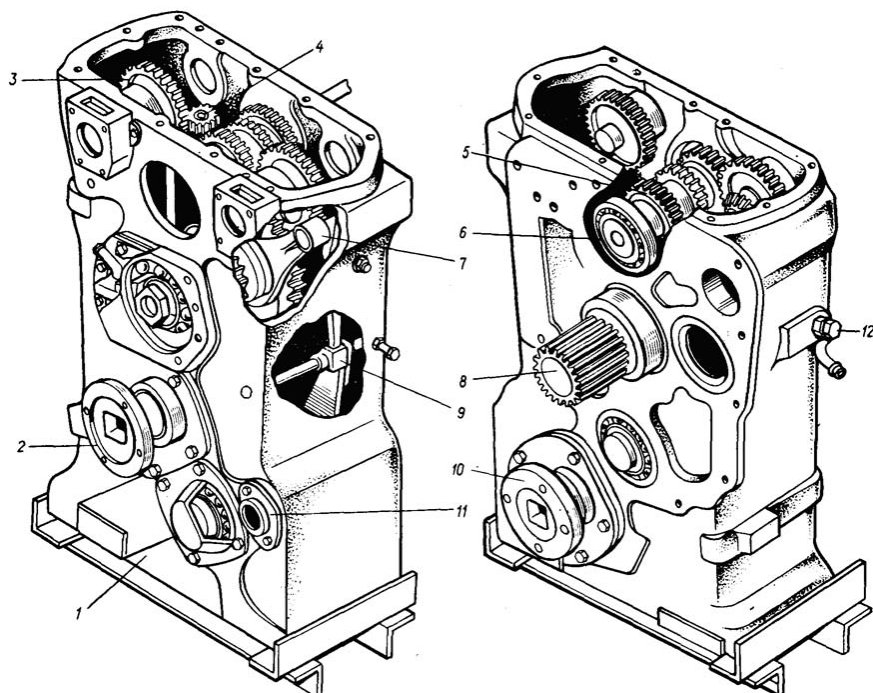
Разборка раздаточной коробки: 1 — корпус; 2 — вал привода заднего моста; 3, 4, 5 — колесо зубчатое; 6 — вал привода ВОМ; 7 — вилка; 8 — вал первичный; 9 — механизм включения переднего моста; 10 — вал привода переднего моста; 11 — указатель уровня масла; 12 — система подвода масла
